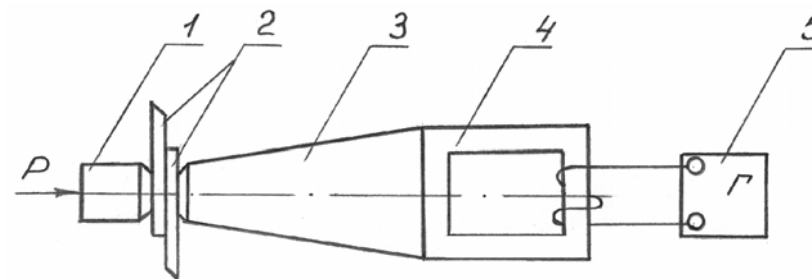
Основной узел ультразвуковой сварочной машины:
